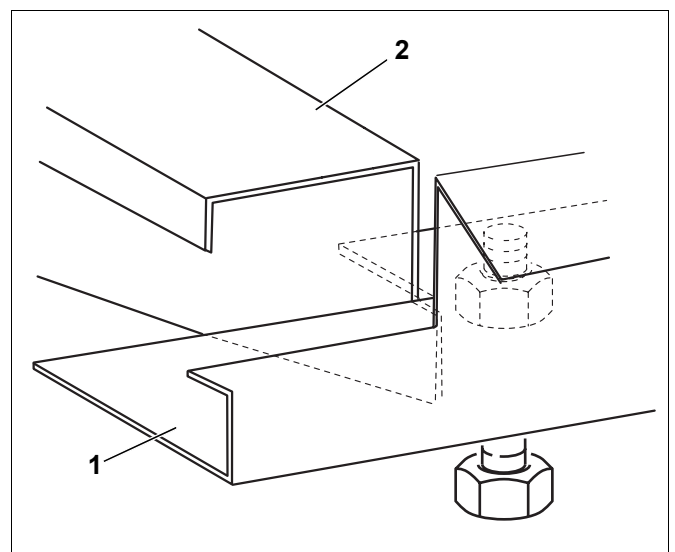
Inserimento della guida longitudinale sulla traversa trasversale
